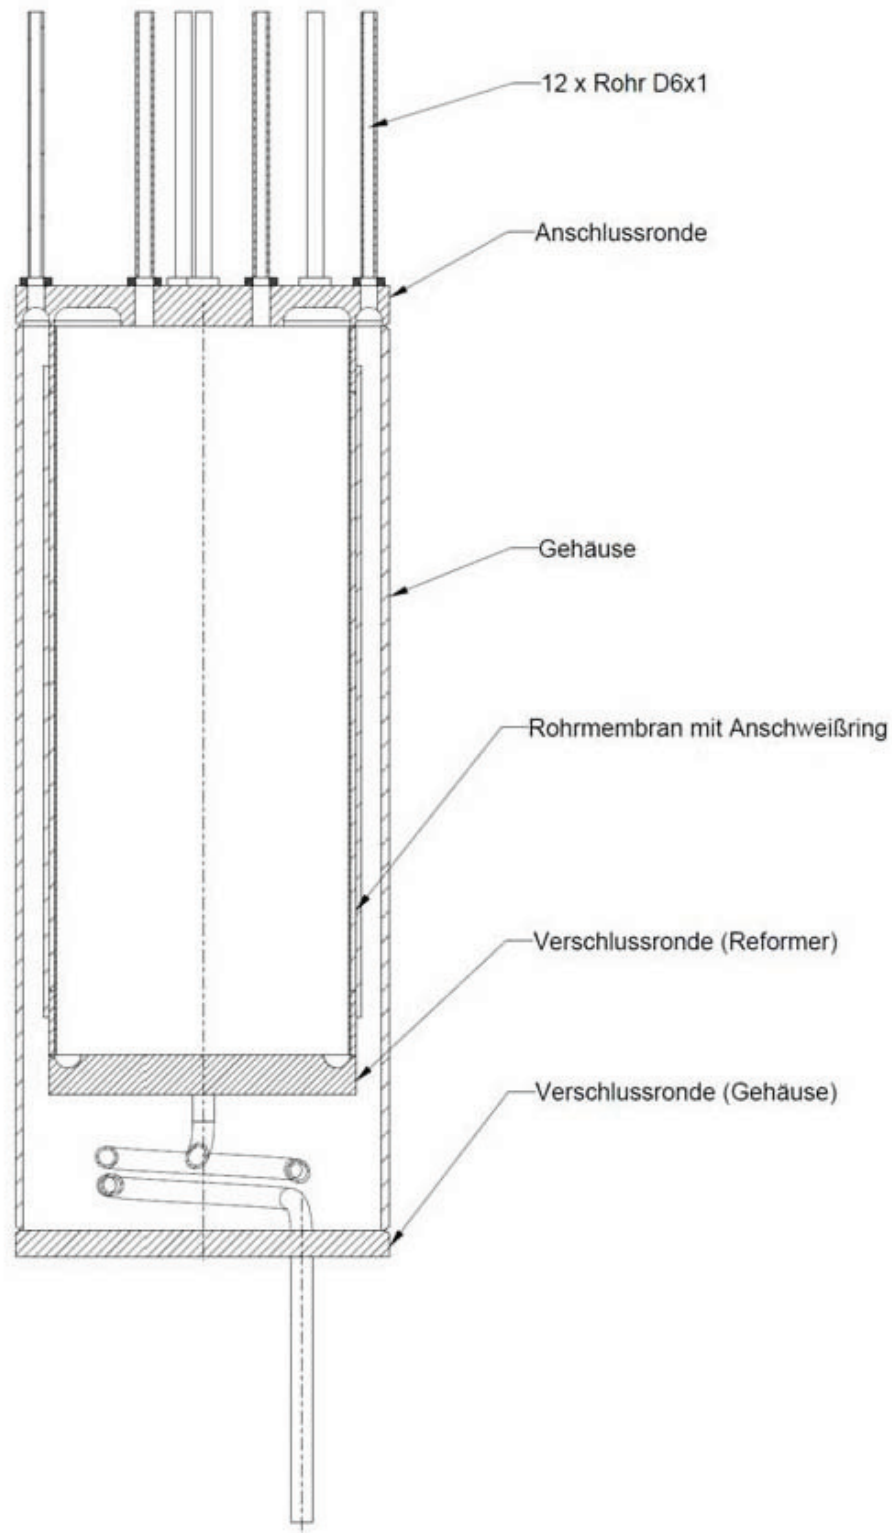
Aufbau der Testkammer mit dem eingeschweißten Rohrmodul
